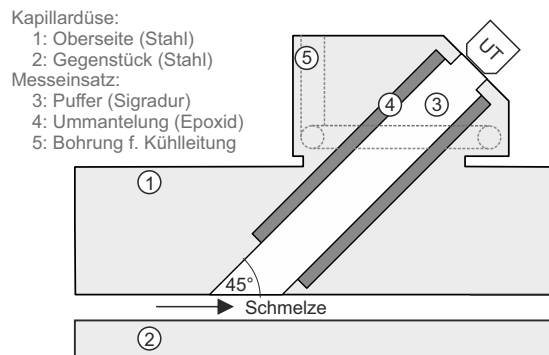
Querschnitt des entwickelten Messeinsatzes.
